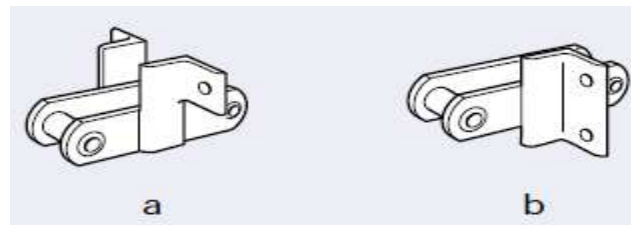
Accesorios tipo F. a) F1, accesorios soldados a placas de unión en uno o ambos lados de la cadena según sea necesario y b) F2, soldadas a placas de unión en uno o ambos lados de la cadena según sea necesario.
